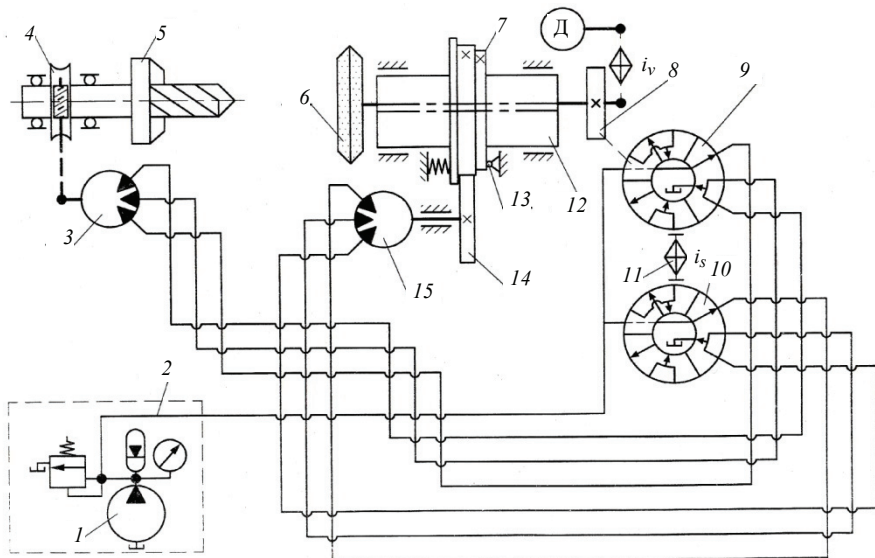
Структурная схема заточного станка с внутренними гидравлическими связями для заточки сверл
